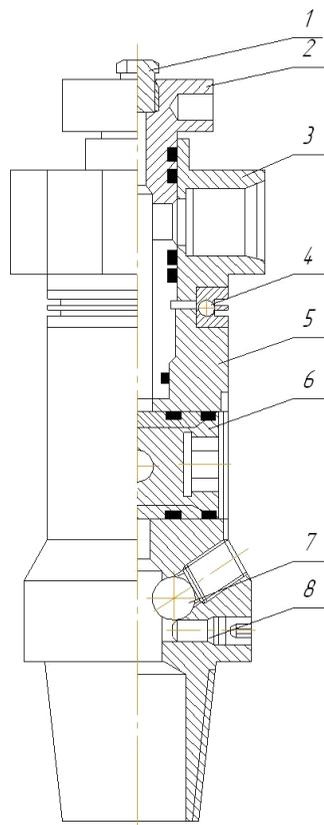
Устьевая, вертлюжная головка: 1 – заглушка, 2 – ствол, 3 – крестовина, 4 – подшипник, 5 – корпус, 6 – пробковый кран, 7 – шар, 8 – винт
